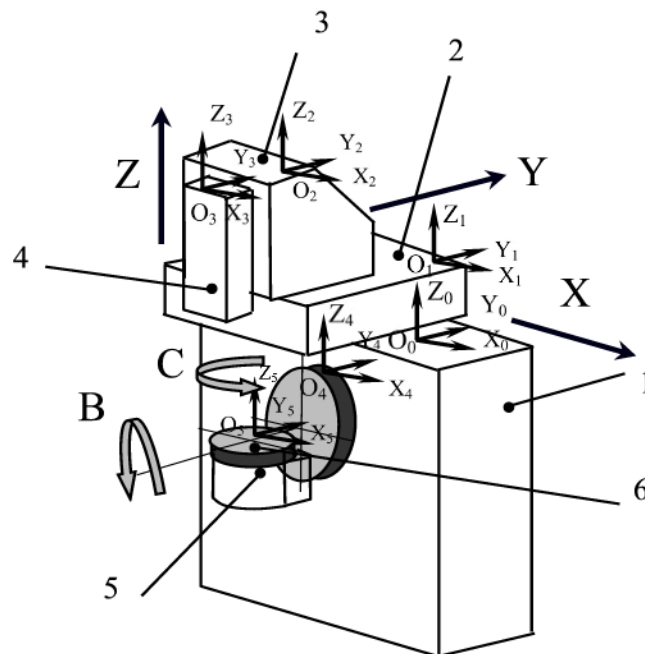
Компоновочная схема станка с системами координат, расположенными на звеньях механизмов несущей системы
